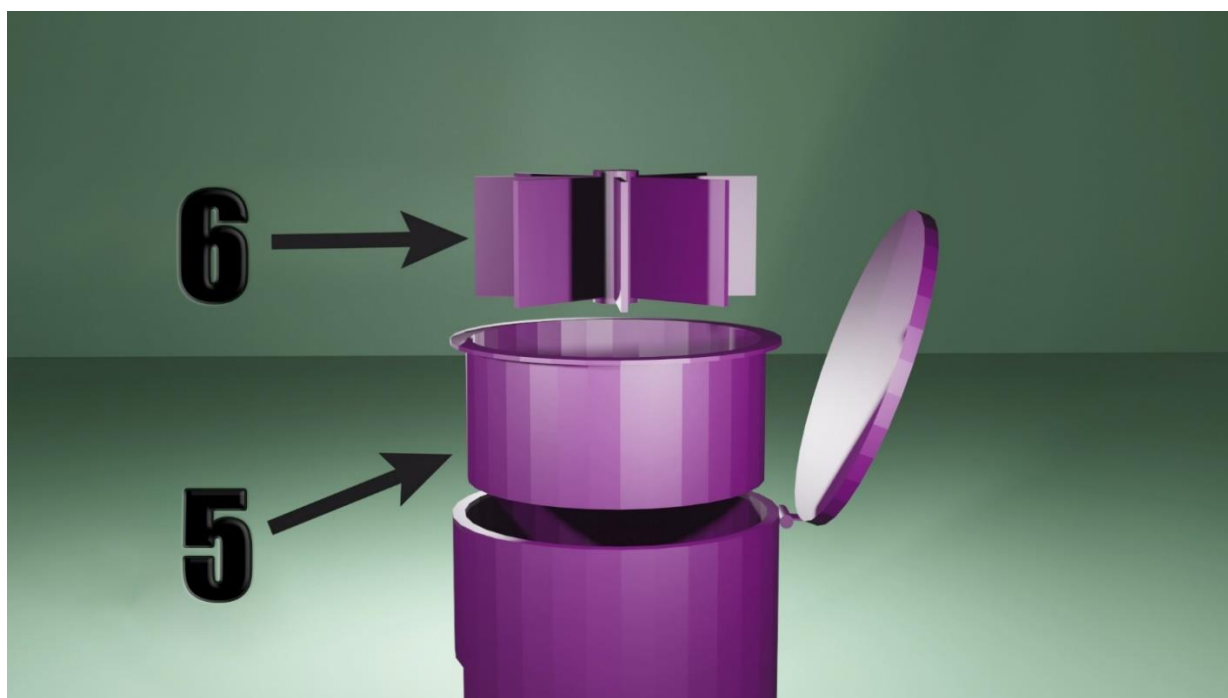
3D-модель внутрішнього барабану Автоматизованого дозатору ліків: 5 – корпус барабану; 6 – лопаті для пігулок
